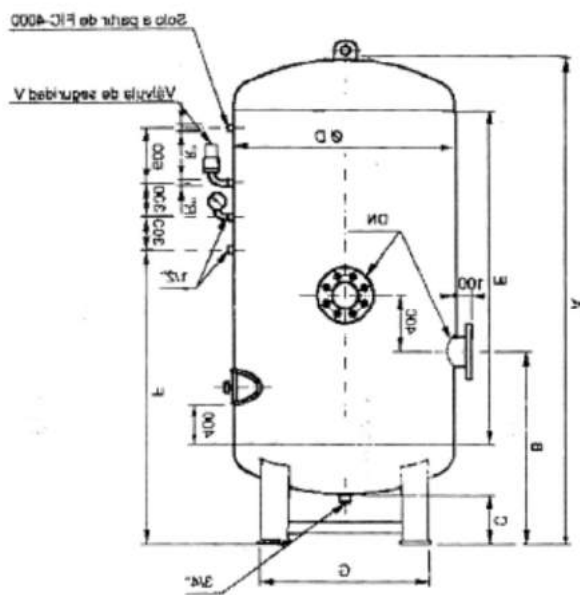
Plano planta conjunto de Calderín compresor.
